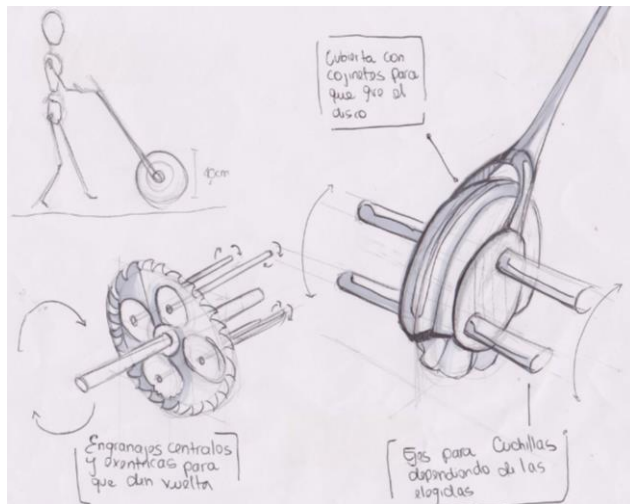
Boceto, máquina con mecanismo. Fuente propia
